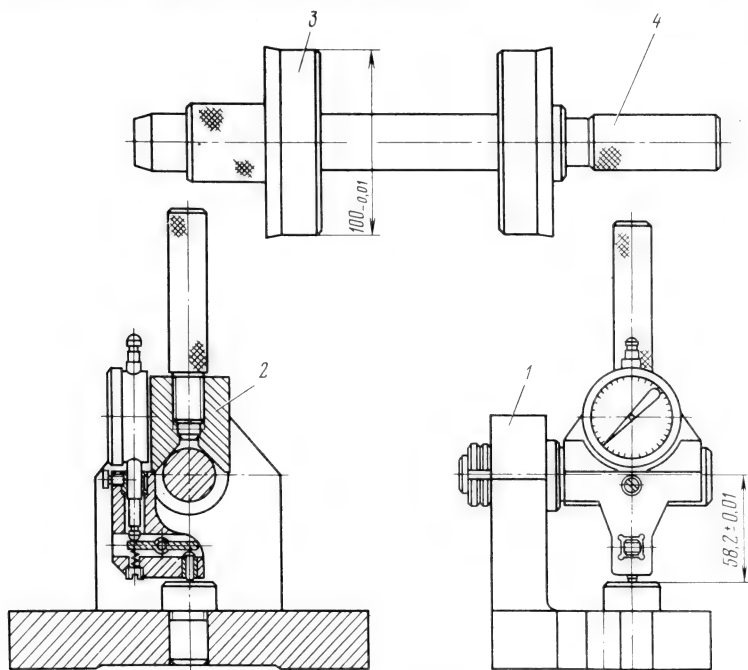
Контрольное приспособление для подбора толщины регулировочной шайбы:
